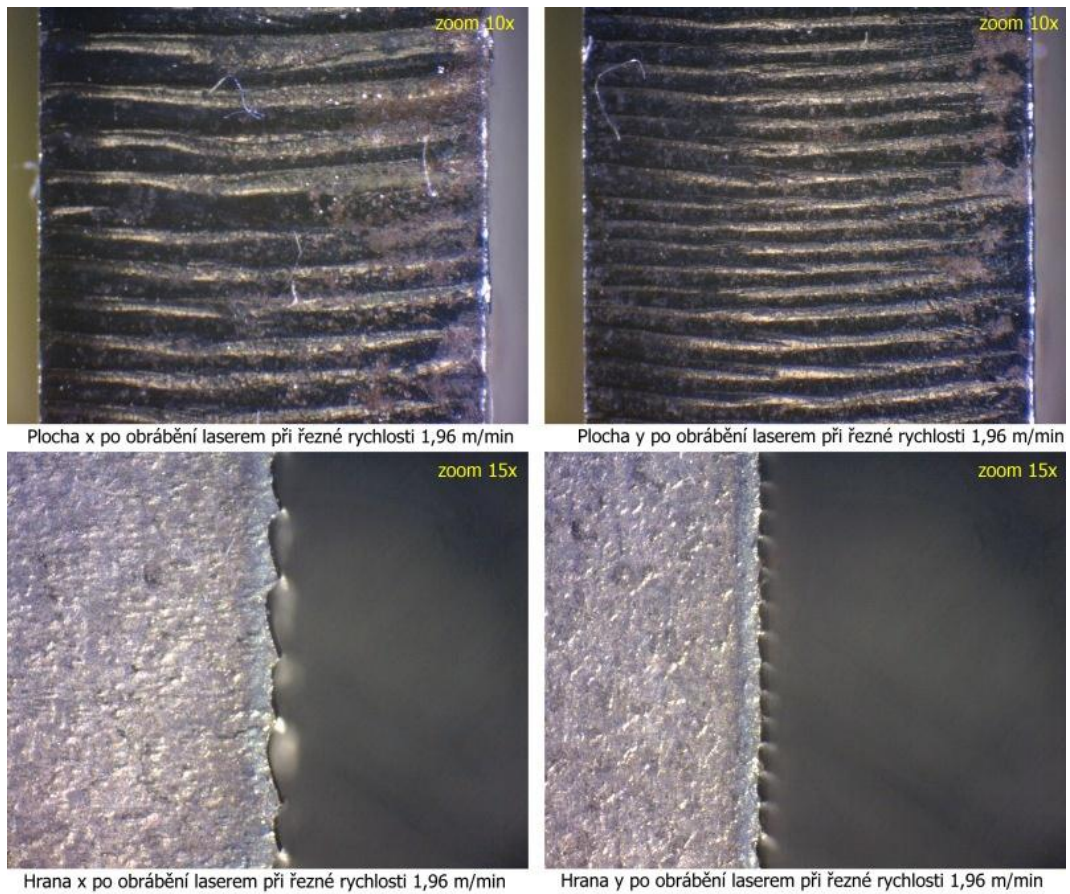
Snímky z mikroskopu vzorku 3 obráběného laserem - materiál 11 375
